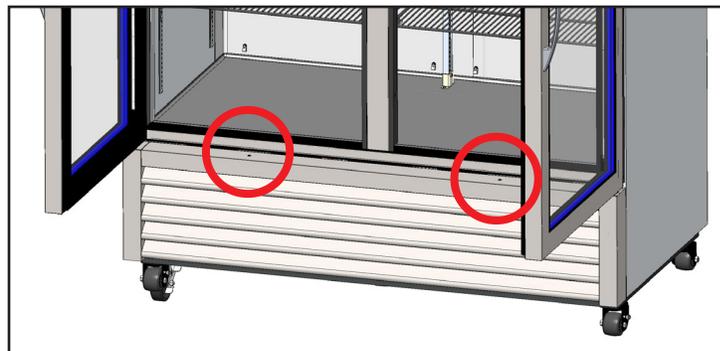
Emplacement des vis de la grille à claire-voie de porte battante.
